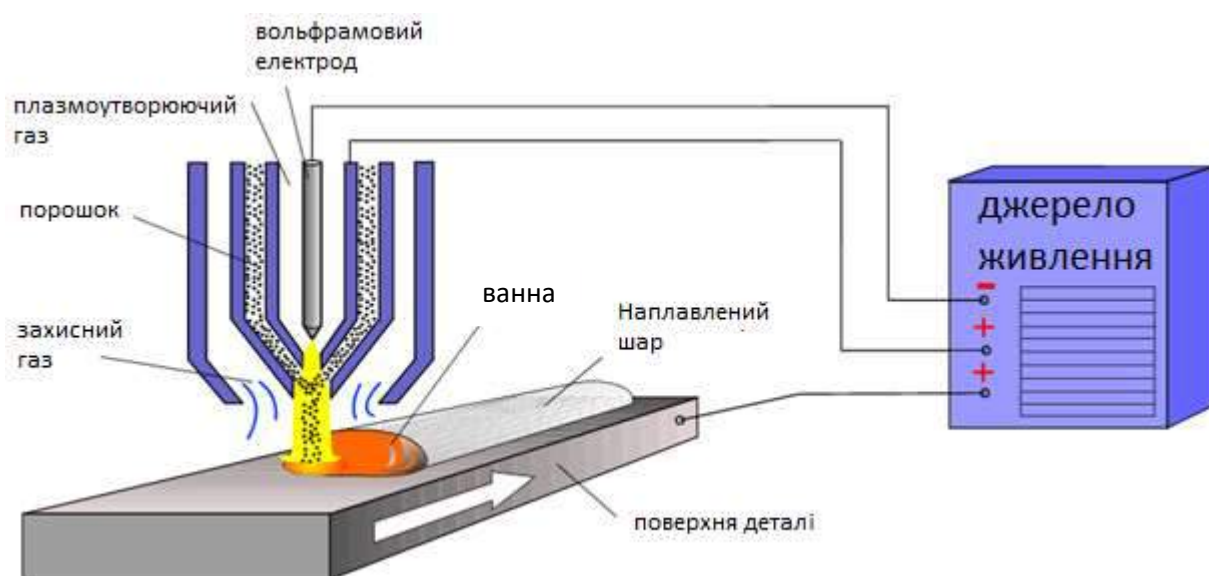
Схема порошково-плазмового наплавлення дугою комбінованої дії
